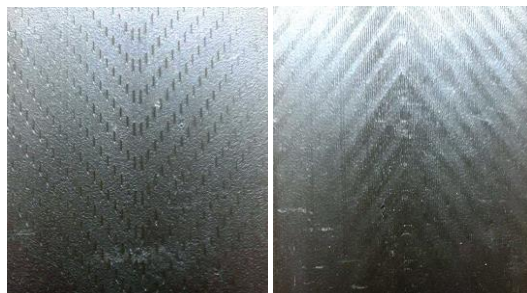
Образцы скользящей поверхности лыж V-образного типа, полученные при помощи накаток.
